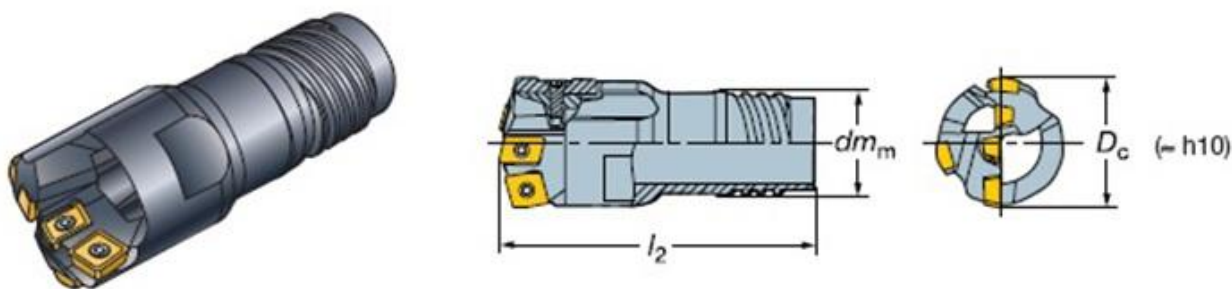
Конструкция головки для глубокого сверления CoroDrill 800.20
